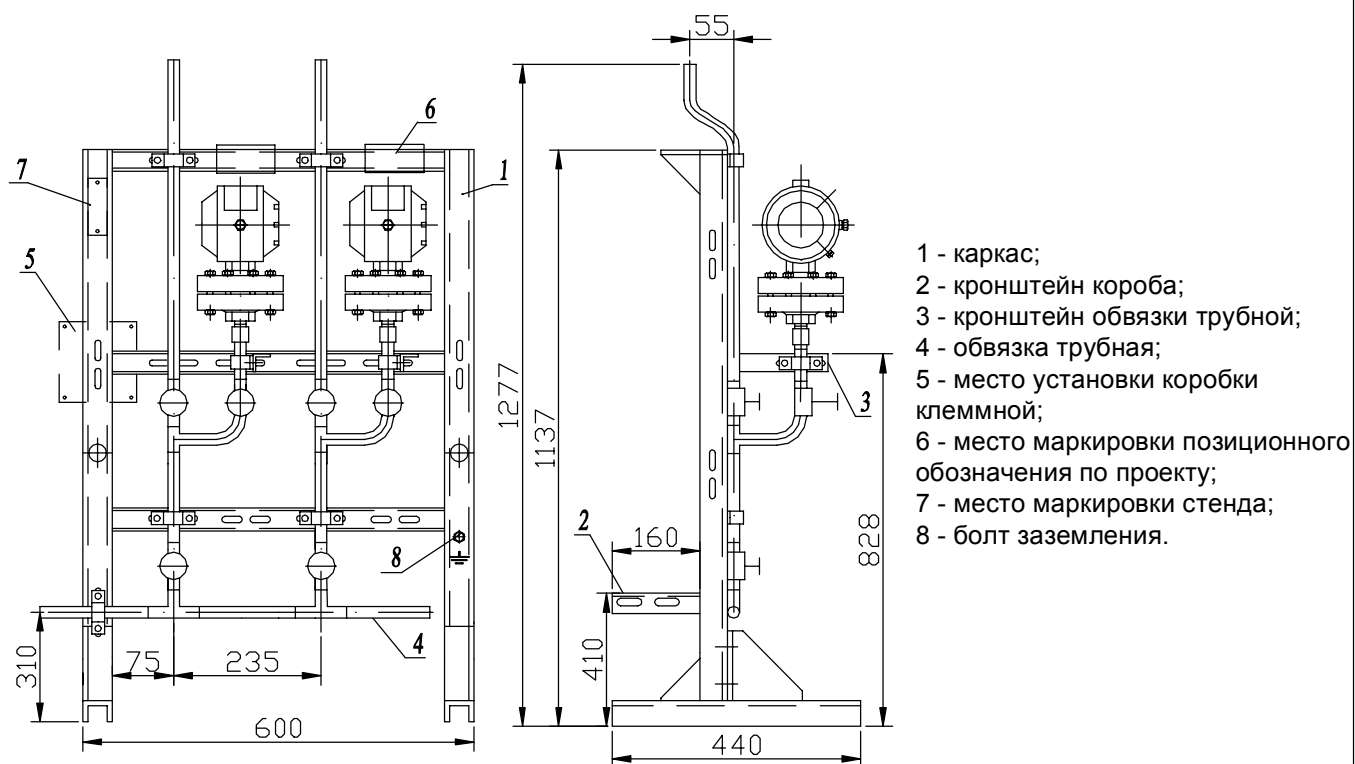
Стенд преобразователей давления с верхним присоединением
